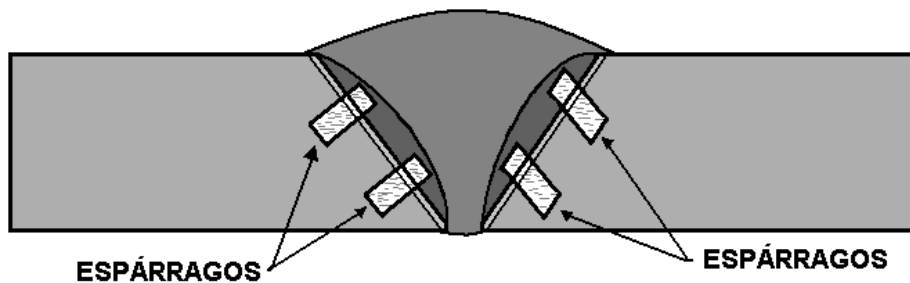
Soldadura en fundición con espárragos insertos
